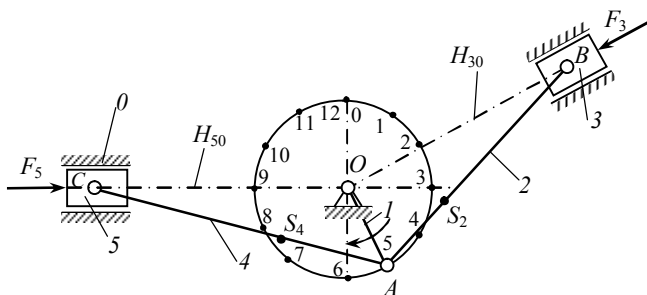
Механизм детандер-компрессора кислородо-добывающей станции
